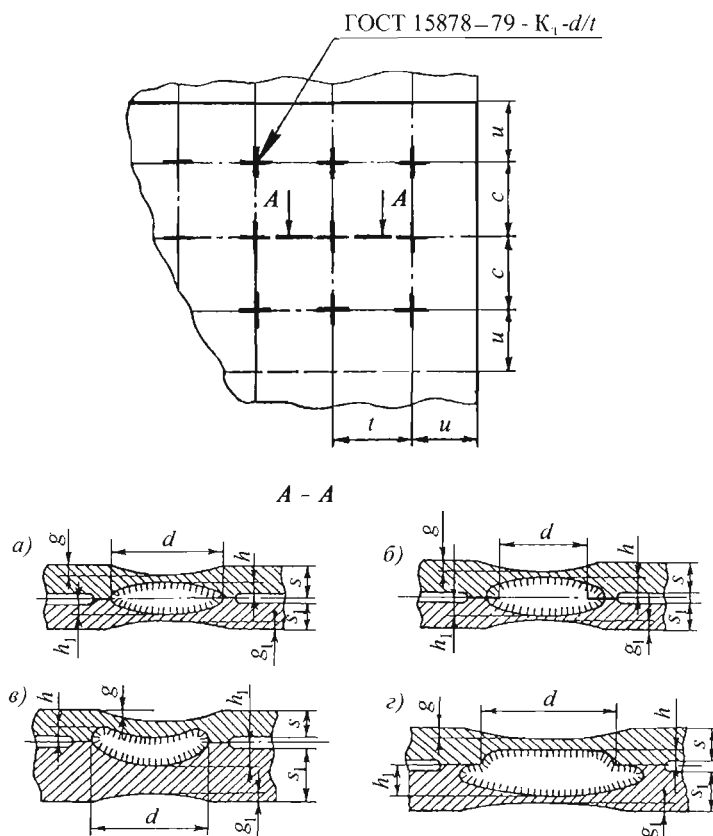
Конструктивные элементы, графическое изображение и условное обозначение сварных соединений, выполненных точечной сваркой из однотолщинных и одноименных металлов (а), плакированного (б) и разноименного металла (в), деталей неравной толщины (г)
